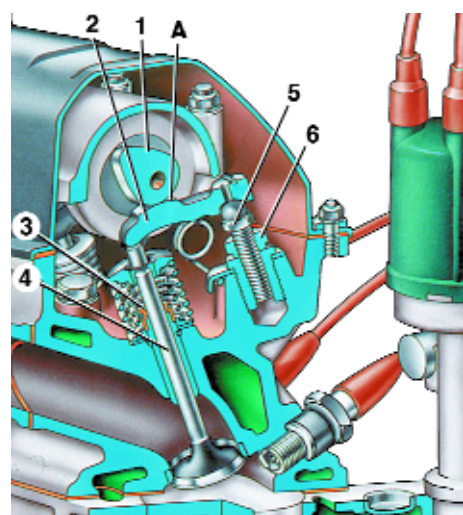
Разрез головки и блока цилиндров двигателя мод. 2106-70 по впускному клапану: 1 – распределительный вал; 2 – рычаг клапана; 3 – маслоотражательный колпачок; 4 – впускной клапан; 5 – регулировочный болт; 6 – контргайка болта; А – зазор между рычагом и кулачком распределительного вала
